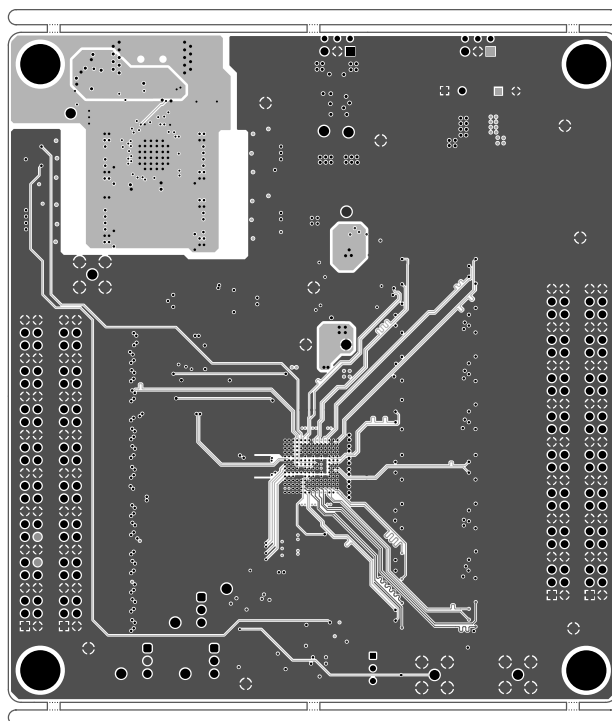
PCB 第 6 层 (接地 3/信号 3)
